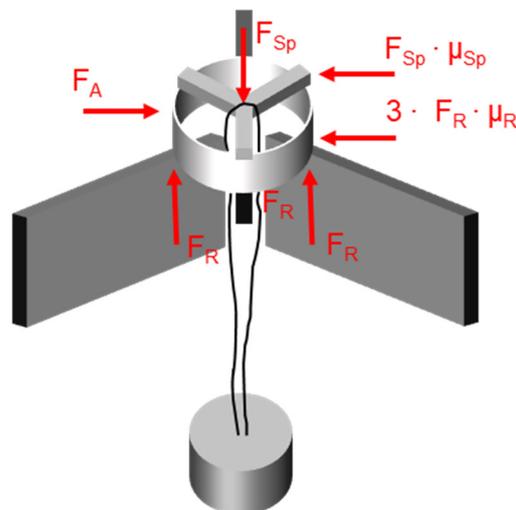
Wirkende Kräfte Dreistegauflage bei horizontaler Antastung. Das Spannkreuz wird mit den Armen versetzt zur Dreistegauflage positioniert.
